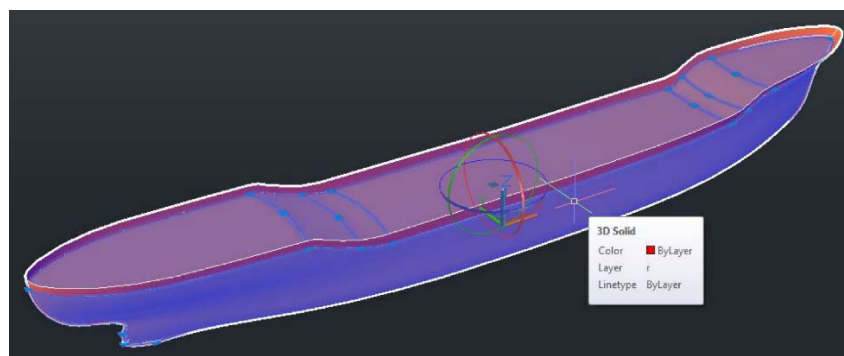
Трехмерная модель корпуса судна в AutoCAD
